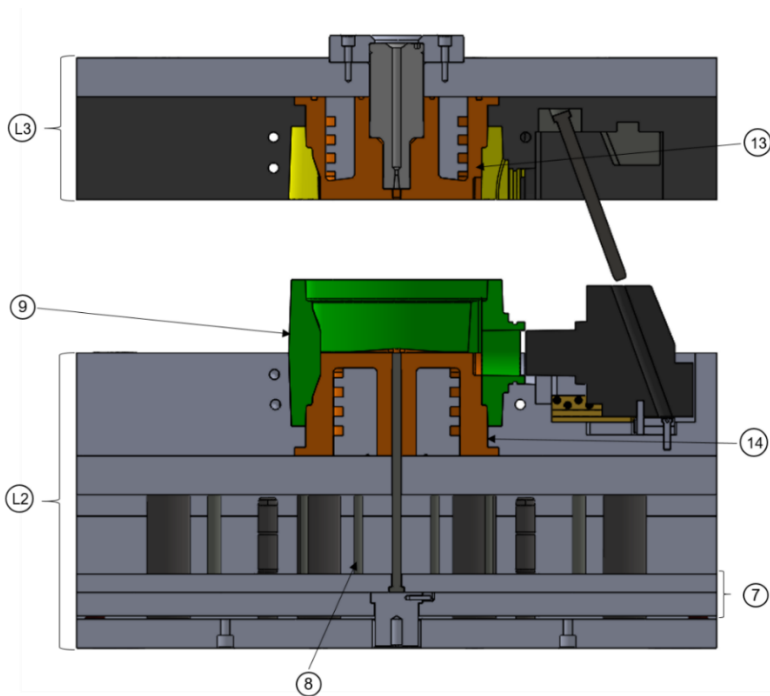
Vista Sección Molde Mecánico, Molde Abierto
